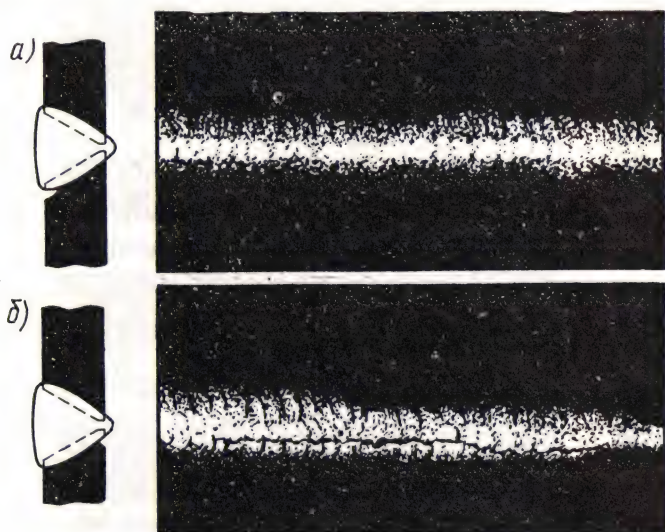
Схема и рентгеновский снимок сварного шва с подрезом (а) и над-
